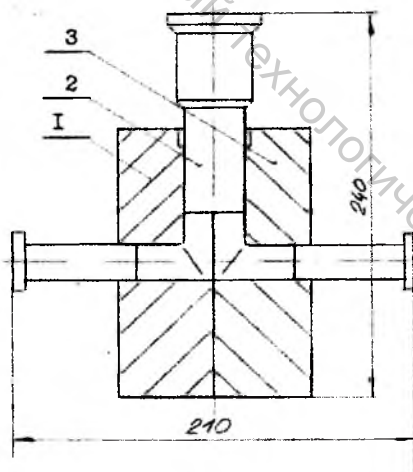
Рабочие части штампа для изготовления поволок тройников в штампах с вертикальным разъемом матриц.
